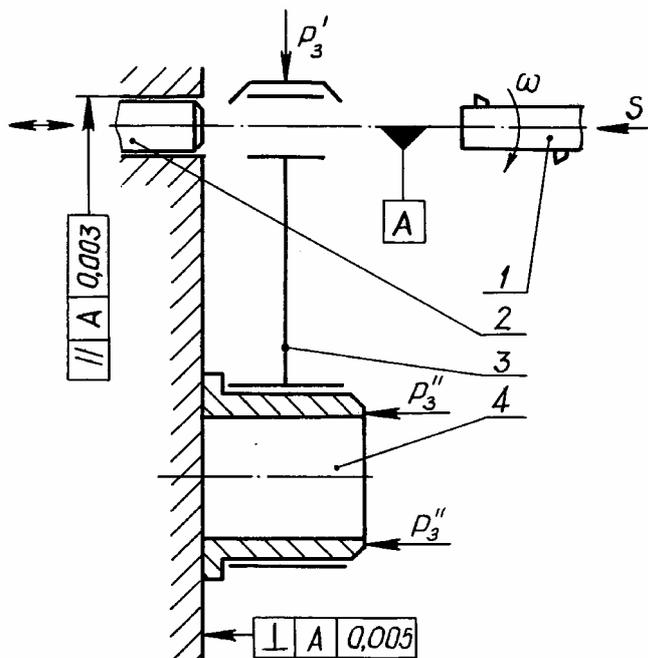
Схема установки шатуна на горизонтально-расточной станок КК-1454 при обработке отверстия в верхней головке: 1 – шпиндель; 2 – центрирующая оправка; 3 – заготовка; 4 – установочная оправка; ω и S – угловая частота и подача шпинделя; P'_3 и P''_3 – силы закрепления
